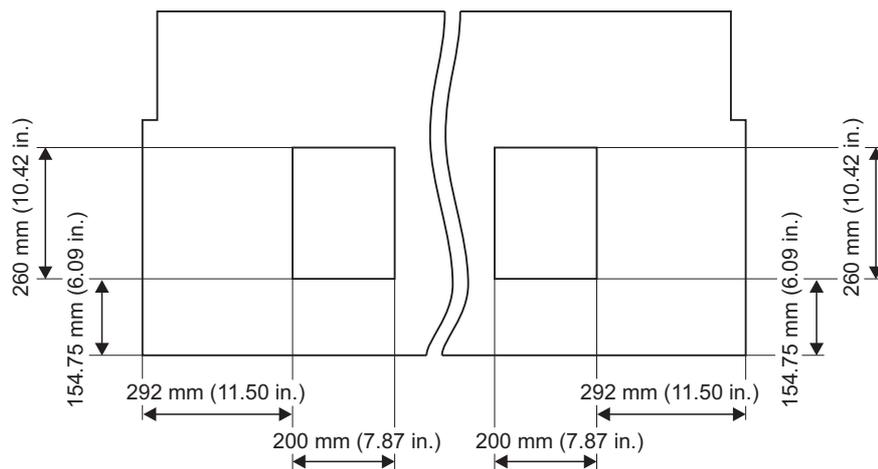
Découpe pour centrifugeuse, sur la droite ou sur la gauche (ou des deux côtés)
